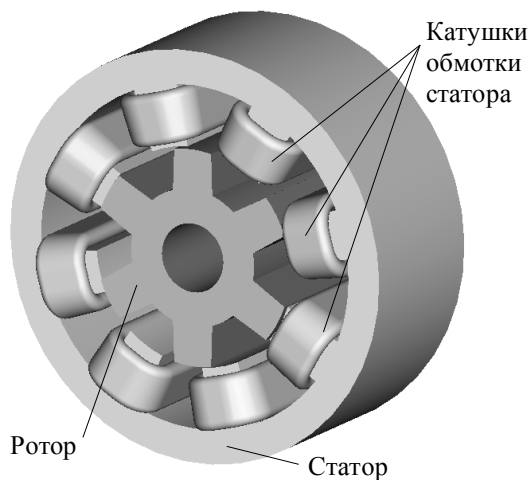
Четырехфазный ЭМП ВРД конструкции 8/6
